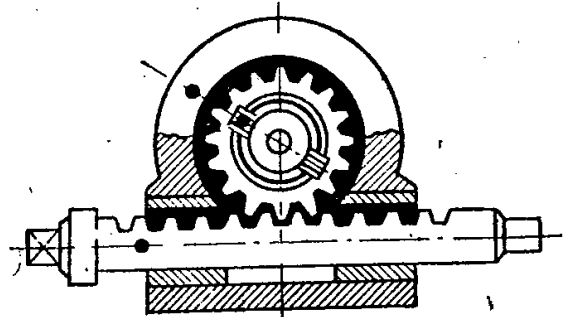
Расположение меток на корпусе секции, рейке и плунжере
